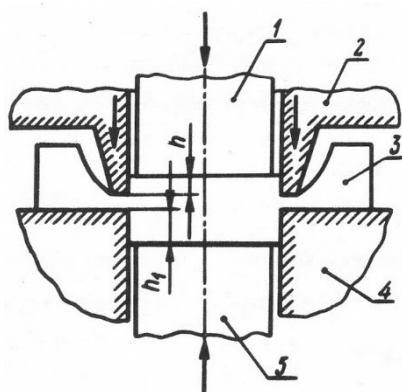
Схема чистовой вырубki встречными матрицами
